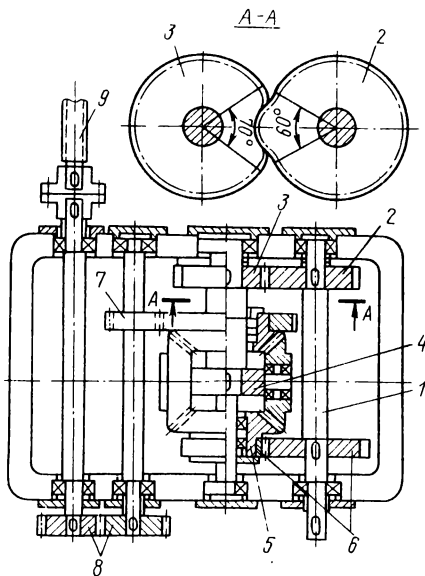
Механизм подачи с некруглыми зубчатыми колесами трехниточного стана ХПТ 12-20
